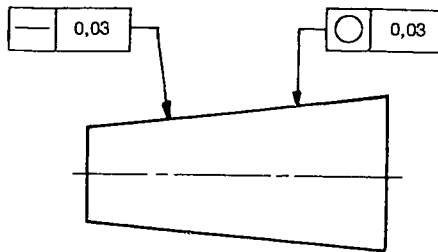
Application du cadre de tolérance aux surfaces inclinées ou coniques
